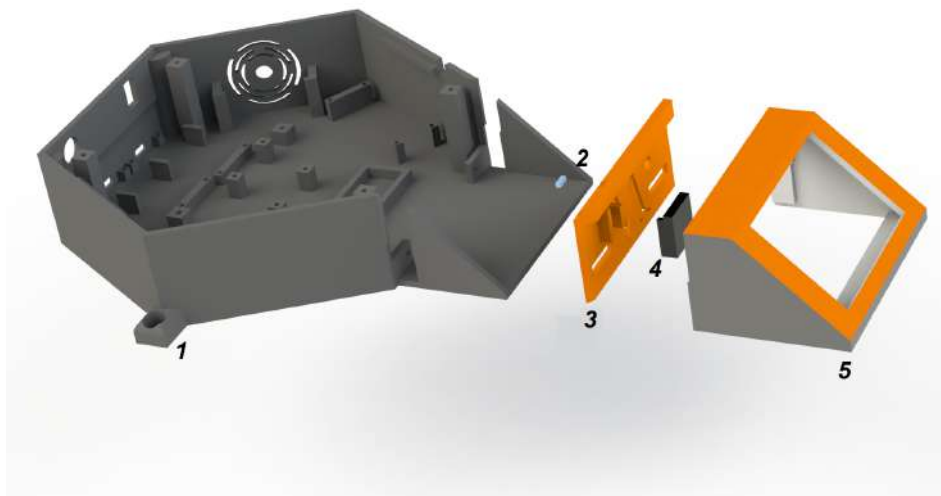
Diseño CAD de la base para ensamble electrónico. Fuente: Elaboración propia
